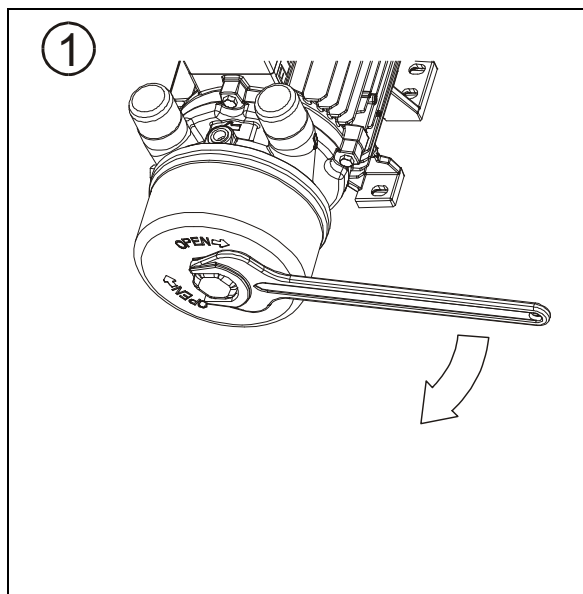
Smontaggio della carcassa della pompa per vuoto / del compressore
